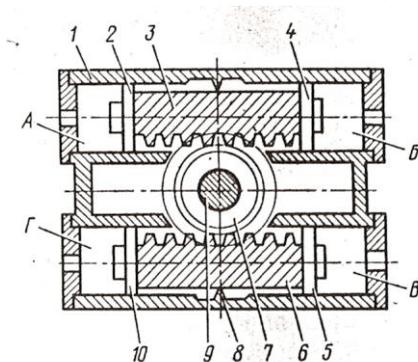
Поршневой поворотный гидродвигатель: 1 - цилиндр; 2, 4, 5, 10 - поршни; 3, 6 - рейки; 7 - шестерни; 8 - упор; 9 - выходной силовой вал.
